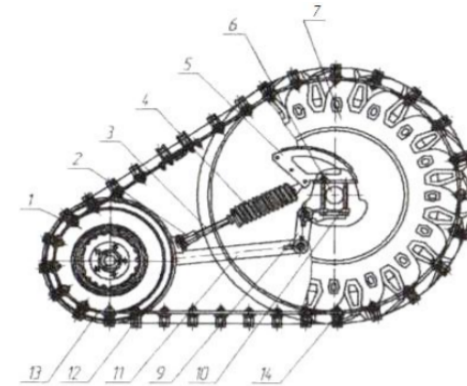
Полугусеничный движитель с резинометаллической гусеницей и штампованными почвозацепами
